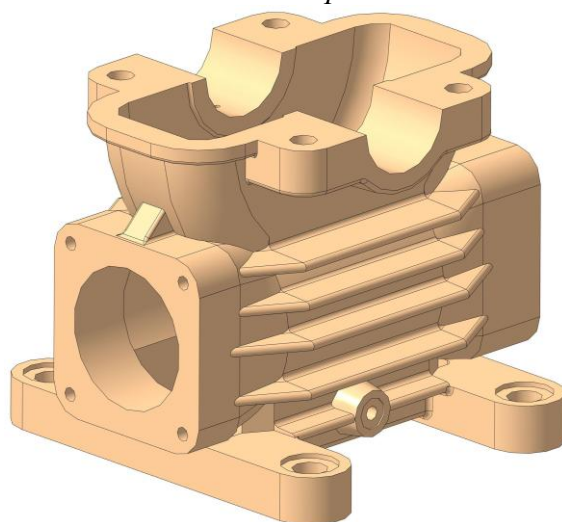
Тривимірна модель корпусу черв'ячного редуктора
